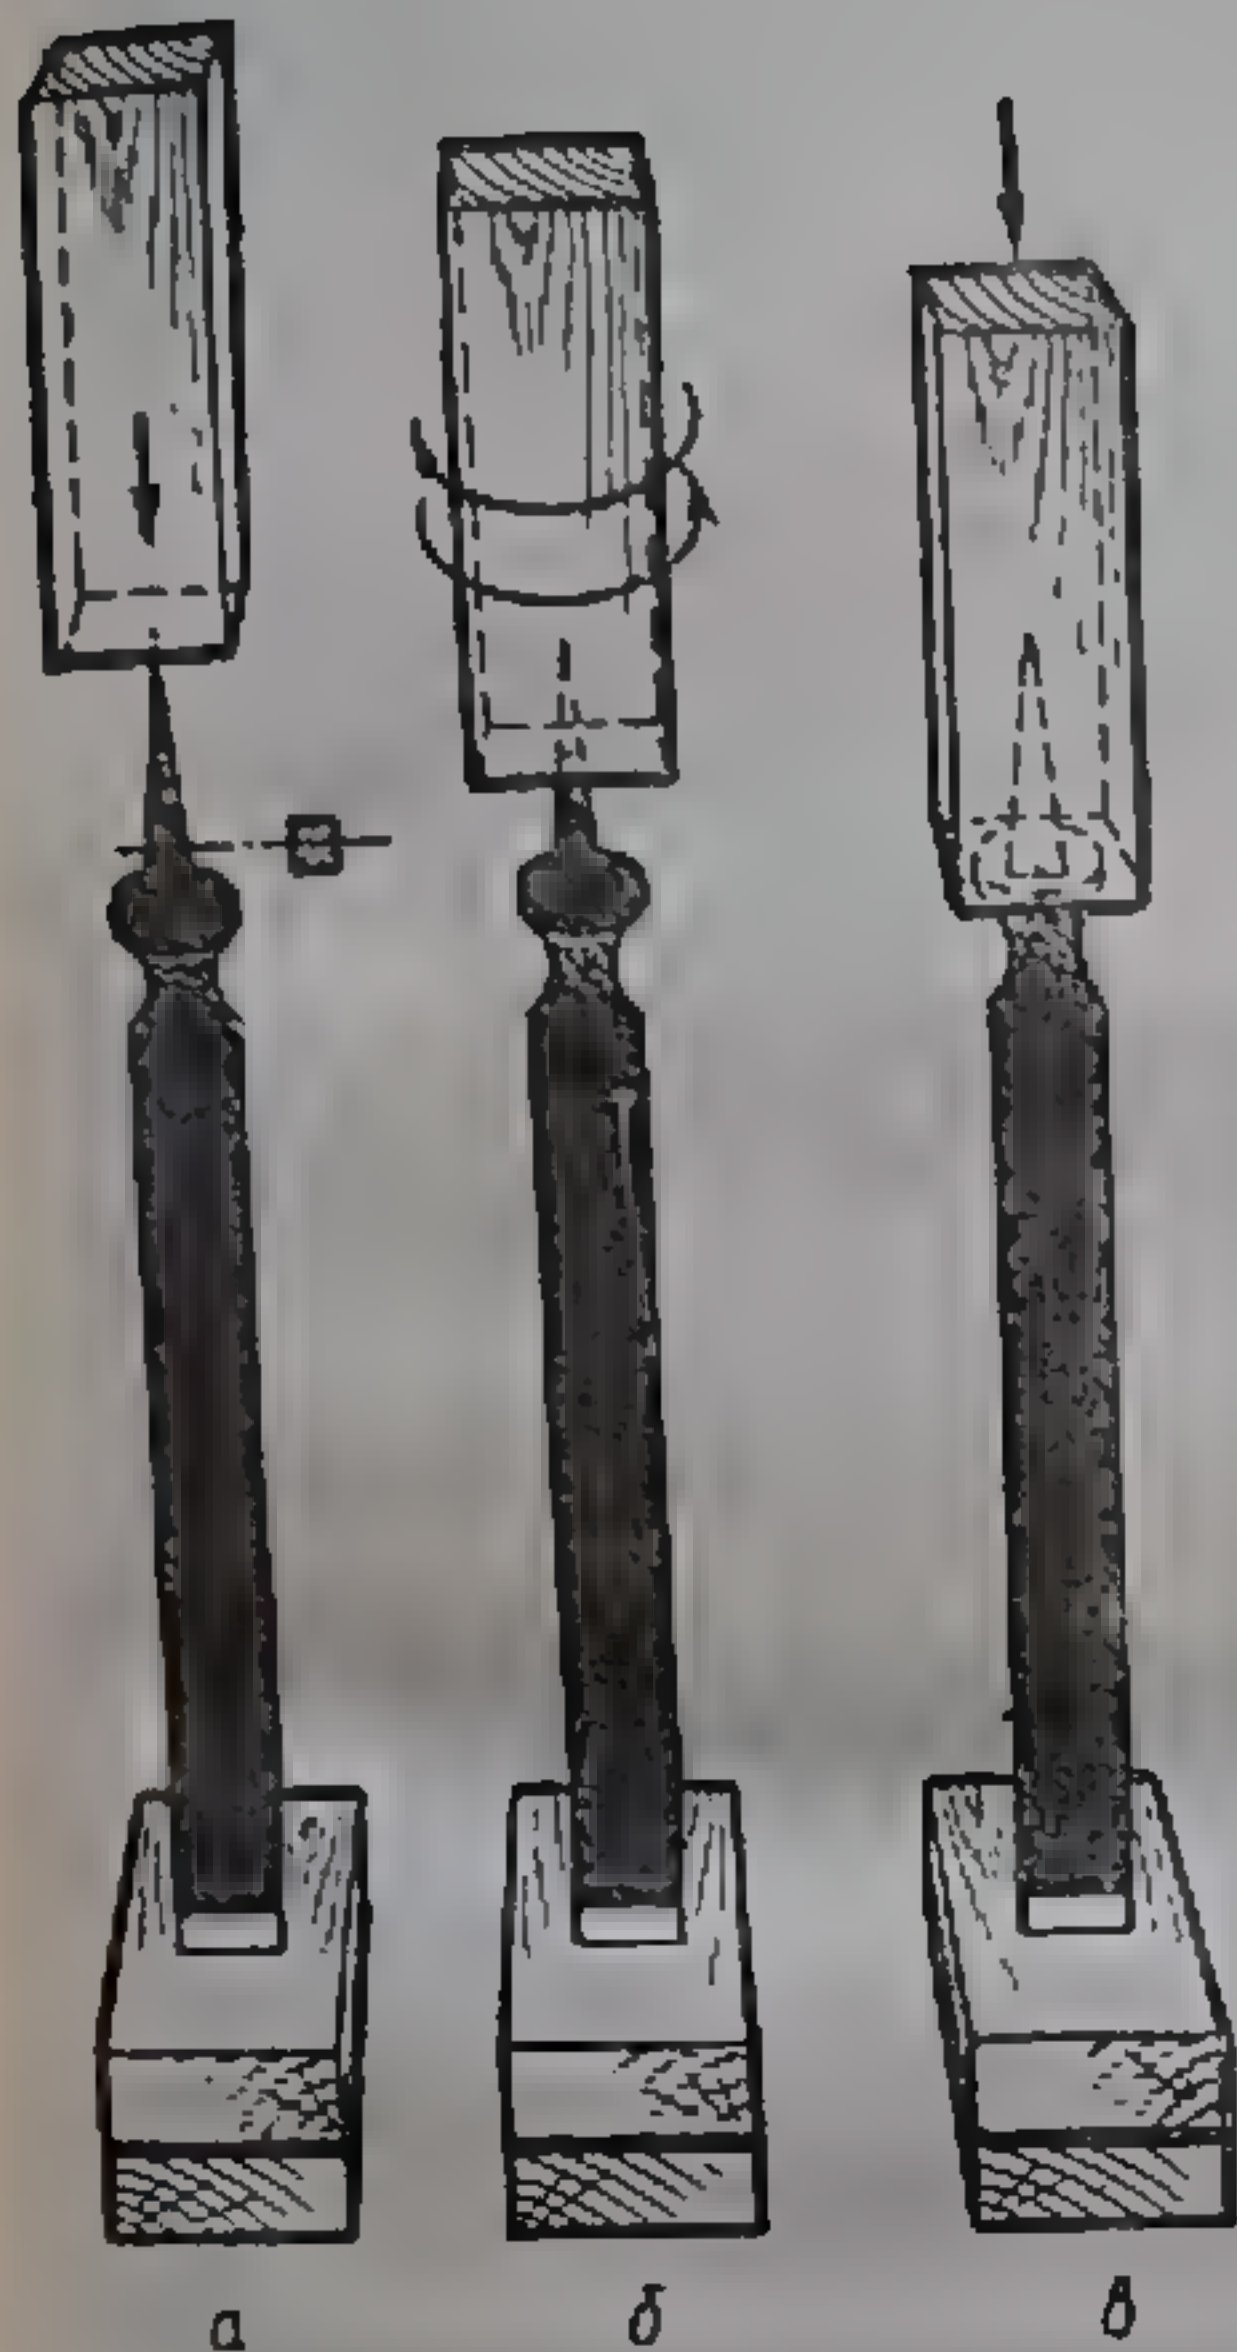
Насадка заготовки на хвостовик квадратного сечения без сверления:
